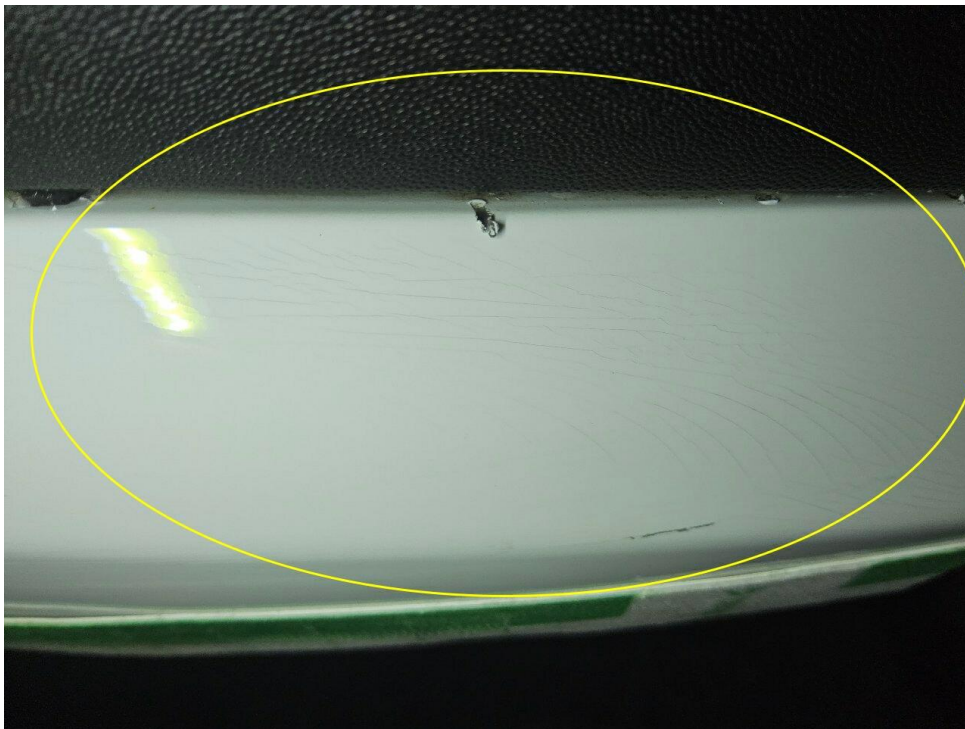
Frontspoiler Lackierung, gerissen, lackieren mit Lackaufbau
